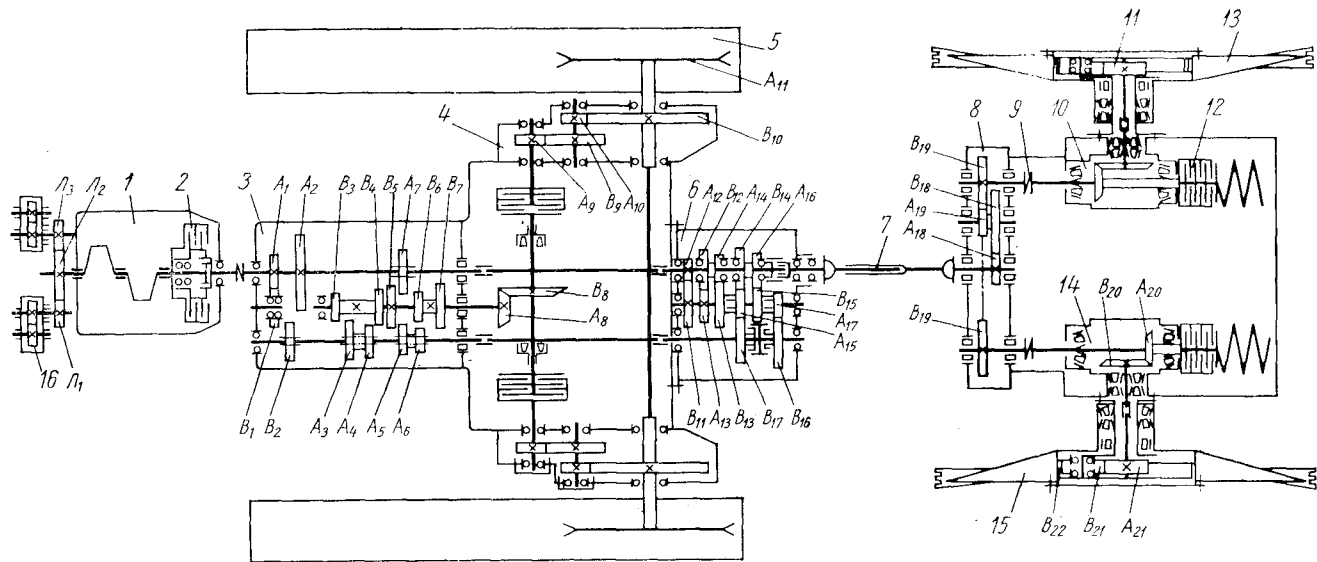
Кинематическая схема силовой передачи трактора и каналоконателя КФН-1200:
